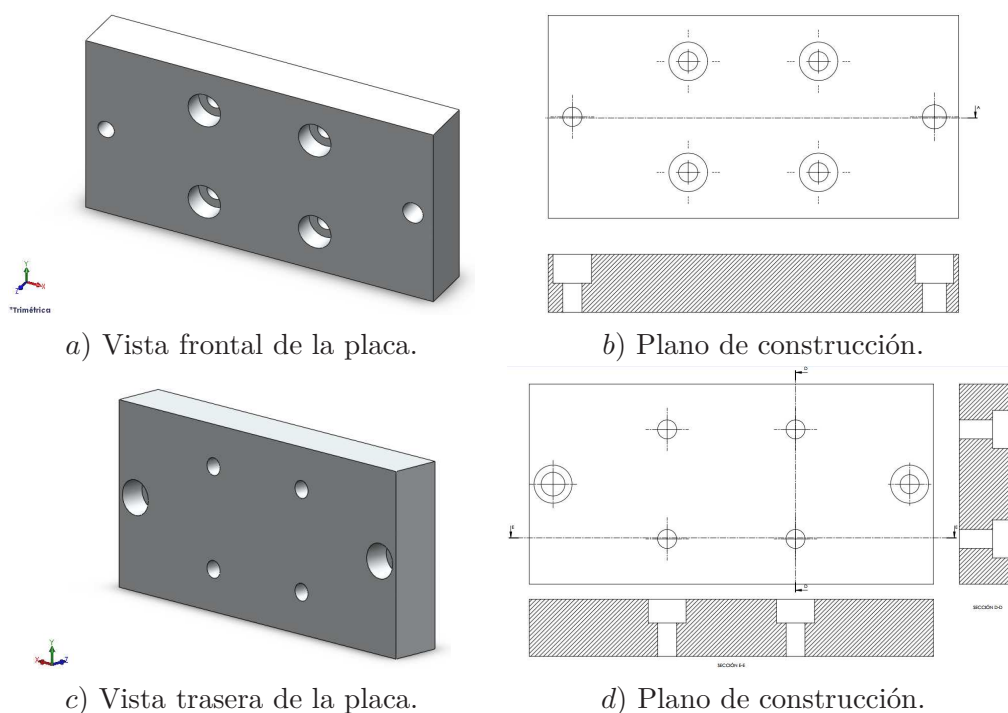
Segunda placa en diseño que será ensamblada con la cámara.
